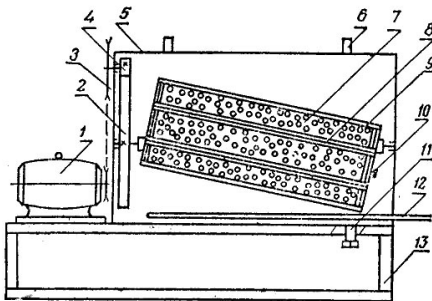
Схема гальтовочного барабана зі зміщеною віссю: 1 – електродвигун; 2 і 4 – шестерні; 3 – клиноремінна передача; 5 – ванна; 6 – упор; 7 – касета; 8 – кутник; 9 – барабан; 10 – болт; 11 – трубка; 12 – змійовик; 13 – рама
